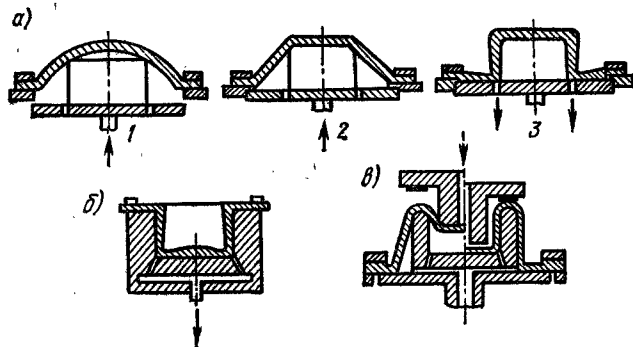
Схема процесса вакуумной формовки: а — позитивный метод; б — негативный метод; в — комбинированный метод; 1 — раздувание нагретой заготовки и подъем пуансона; 2 — формовка пуансоном; 3 — вакуумная формовка
